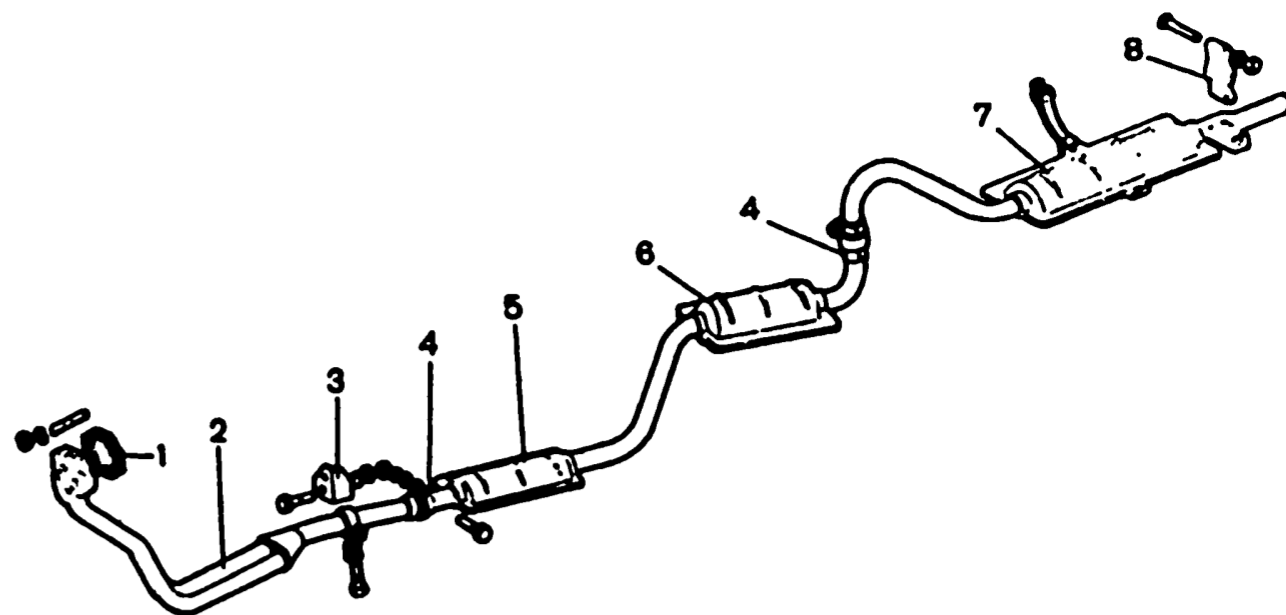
Система выпуска газов автомобиля ВАЗ-21053: 1 - прокладка; 2 - приемная труба глушителей; 3 - кронштейн крепления приемной трубы глушителей к коробке передач; 4 - хомут для соединения труб глушителей; 5 - передний дополнительный глушитель; 6 - задний дополнительный глушитель; 7 - основной глушитель; 8 - подушка крепления выпускной трубы глушителей
